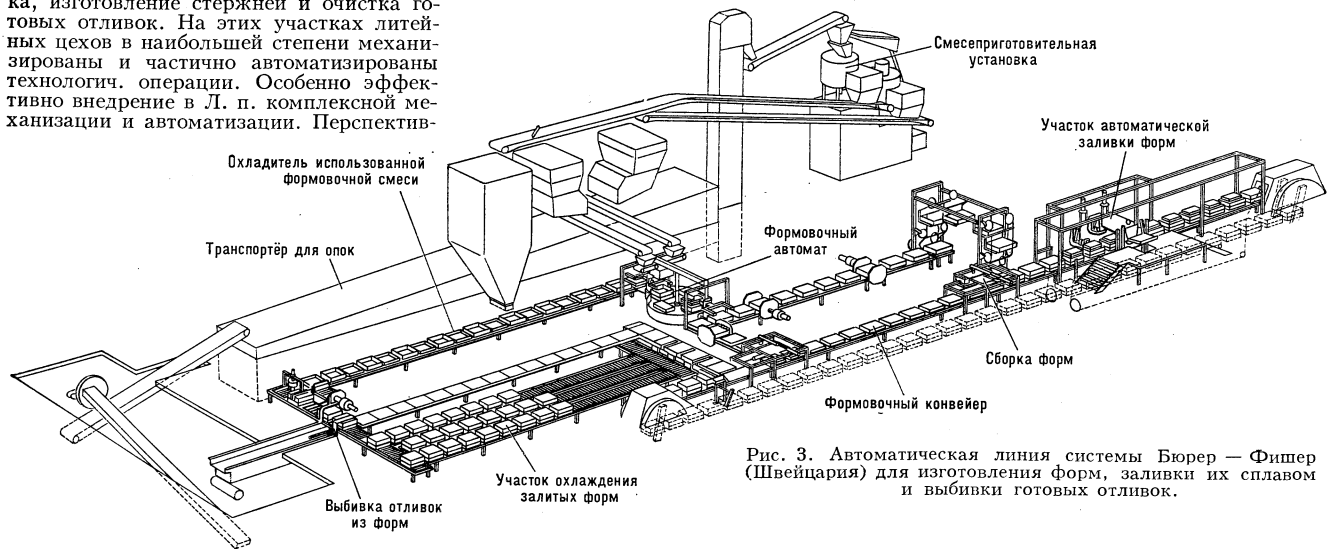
Автоматическая линия системы Бюрер — Фишер (Швейцария) для изготовления форм, заливки их сплавом и выбивки готовых отливок.
